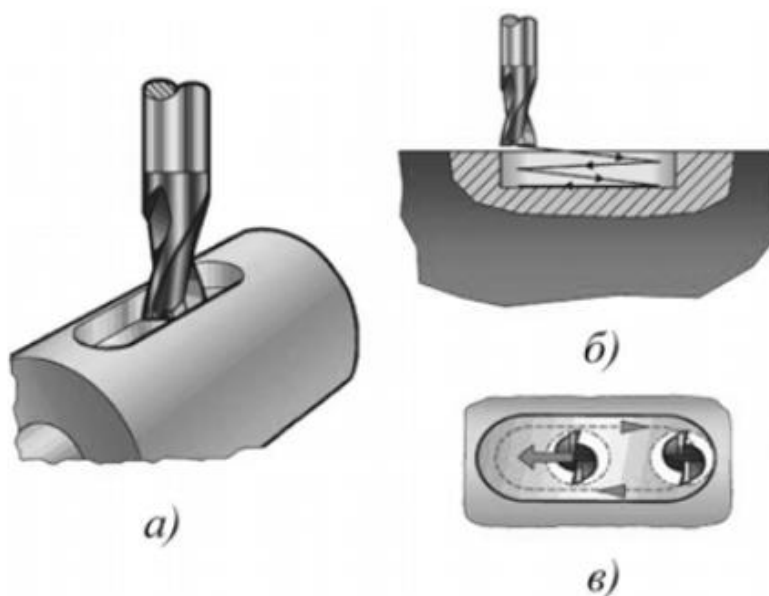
Обработка шпоночных пазов: а – общий вид фрезерования паза; б – схема врезания фрезы; в – схема перемещения фрезы в горизонтальной плоскости паза
